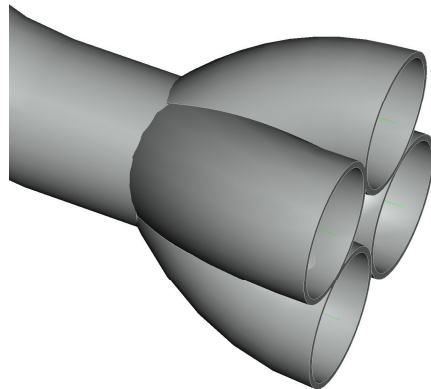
a Obr. 57 Přední a zadní pohled na uspořádání svodů výfuku
